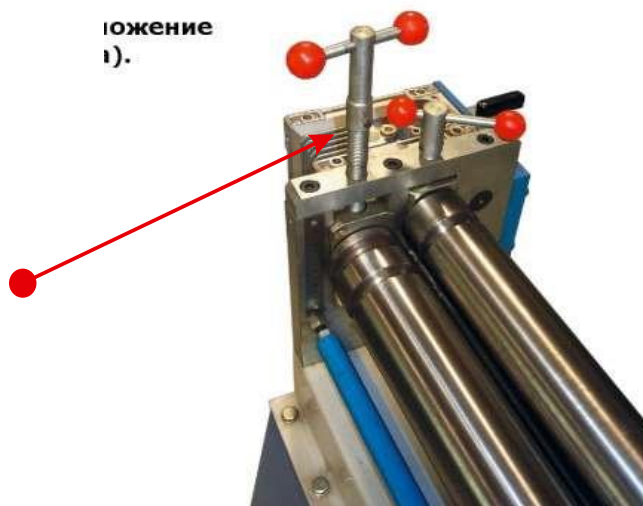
Ручка регулирующая положение заднего вала (вид справа)
